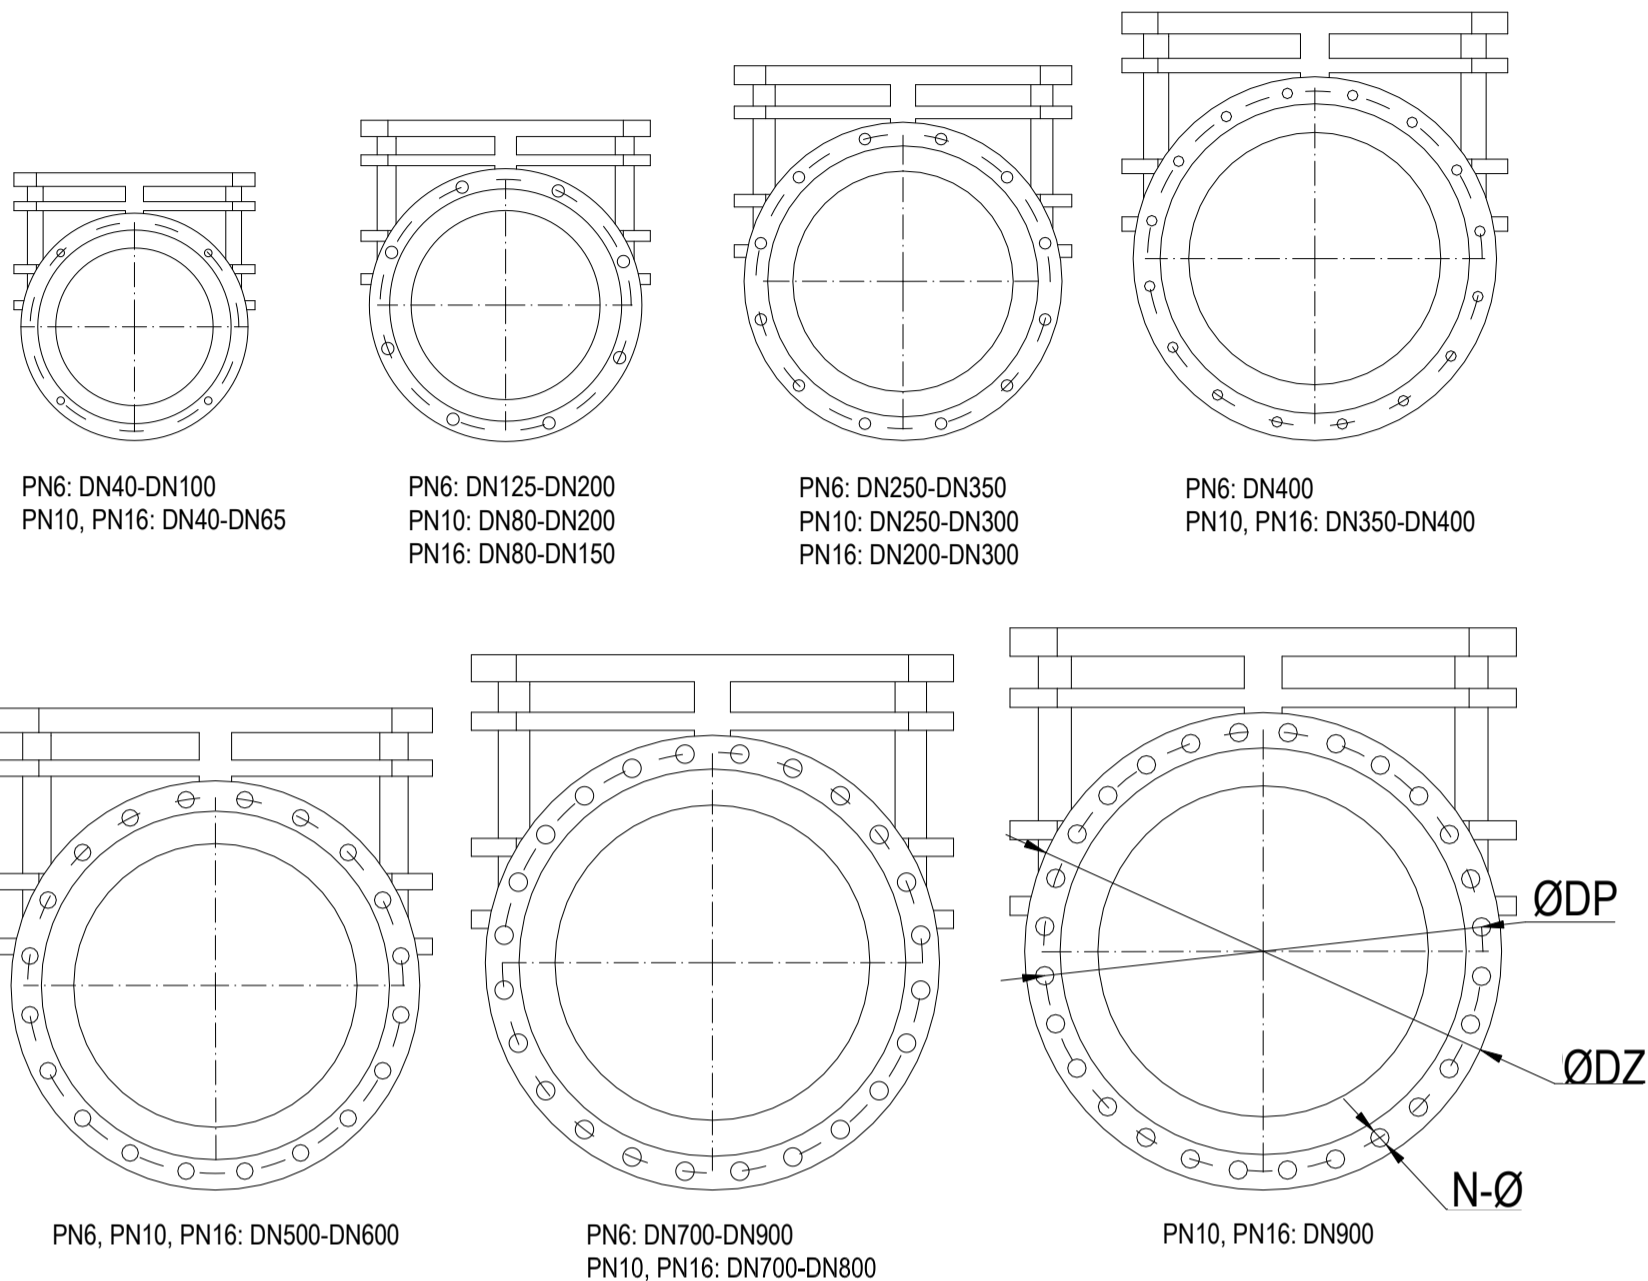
Główne wymiary urządzenia | Main device dimensions | Основные размеры устройства
